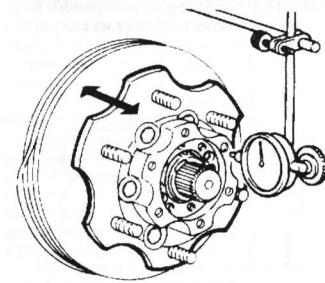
Используйте измерительный прибор для проверки осевого люфта ступицы
